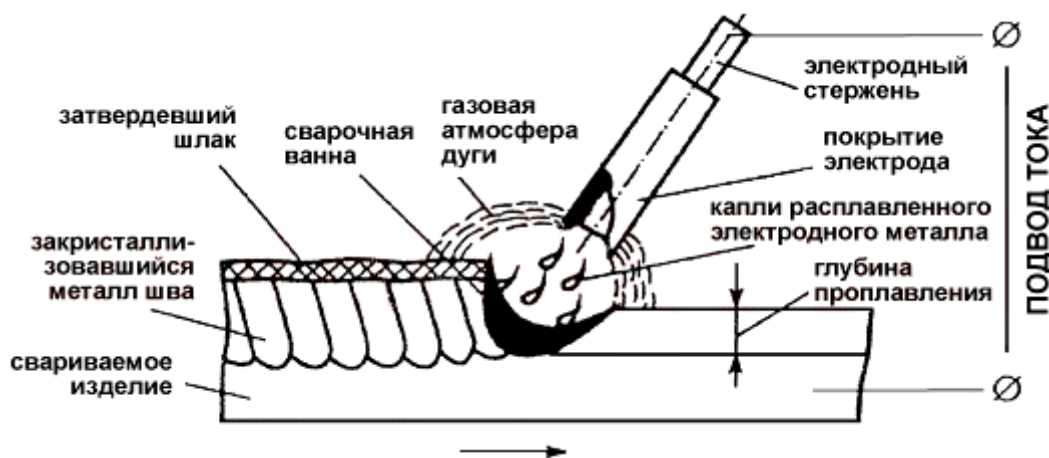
Ручная дуговая сварка штучными электродами
